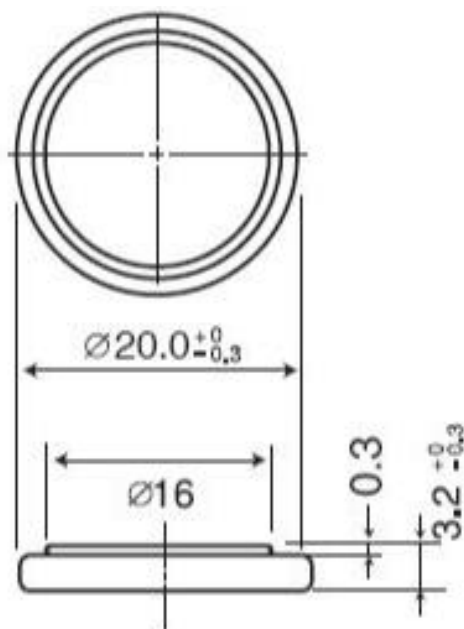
Габаритні розміри батарейки CR2032-7C5
